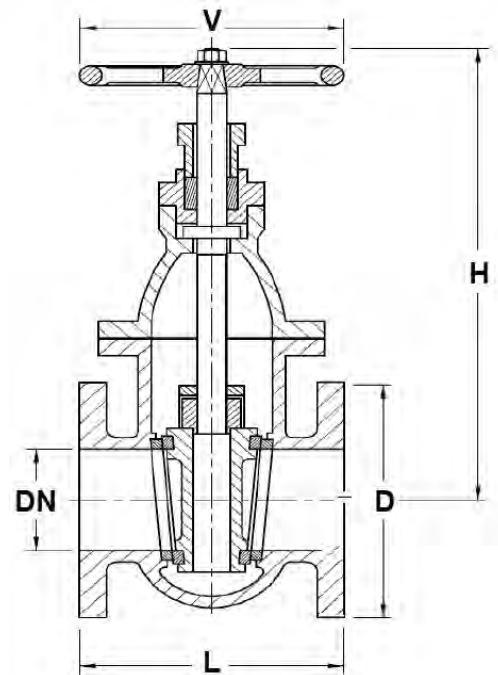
FIGURA DRAWING	CUERPO BODY	CUÑA WEDGE	ASIENTOS SEAT	HUSILLO STEM	TORNILLERIA BOLTING	VOLANTE HAND WHEEL
